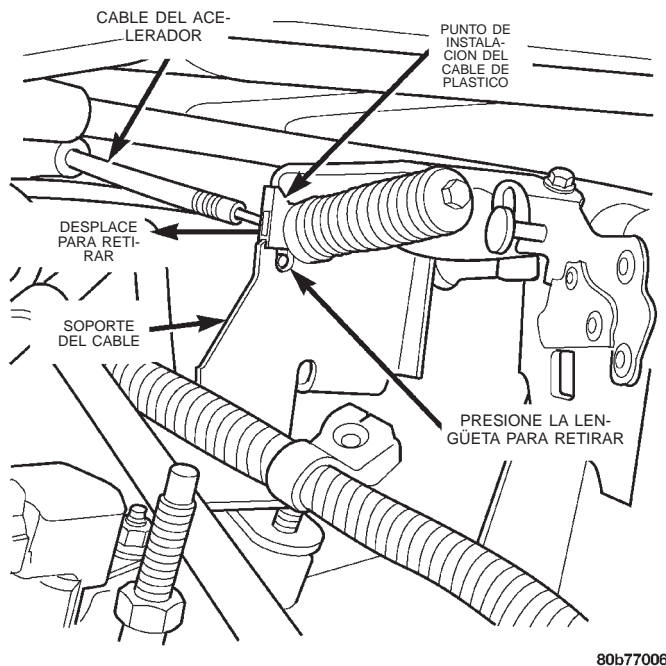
Lengüeta de desenganche del cable del acelerador—Motor 4.7L V-8
